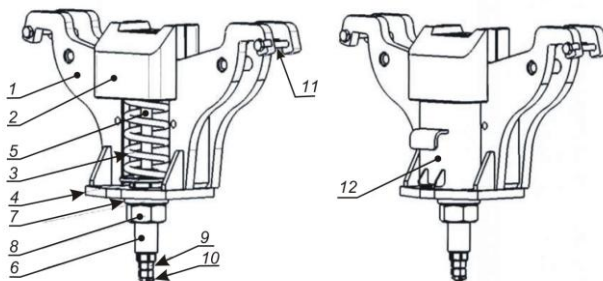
Центрирующий прибор для моторвагонного подвижного состава:
